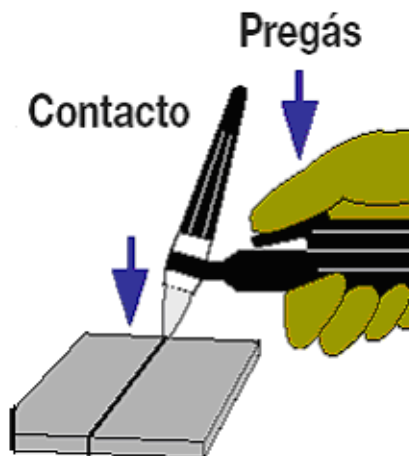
Contacto sobre la superficie para encender el arco de soldadura.
